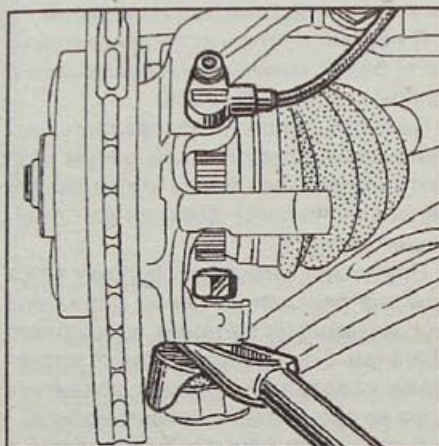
Использование ударного съемника для выпрессовки нижнего шарового шарнира
